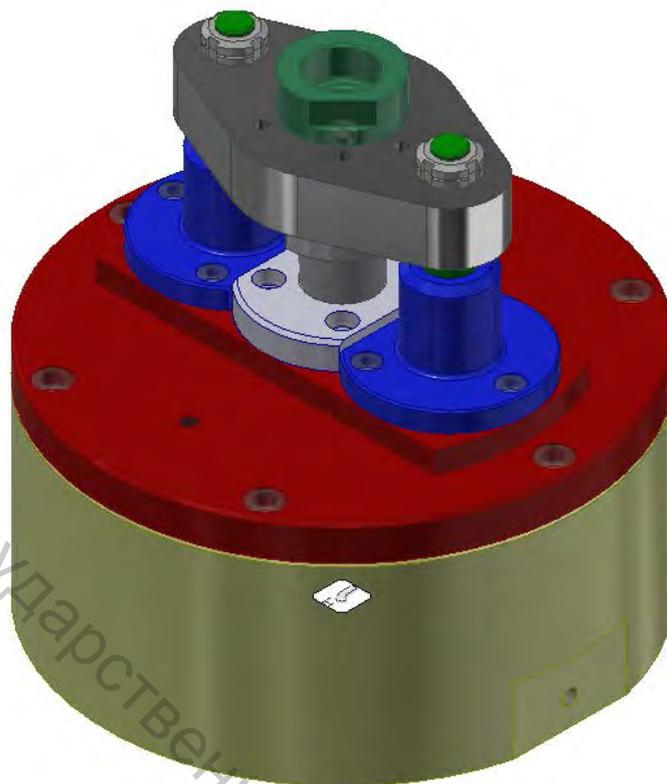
Кондуктор для зенкерования отверстий
